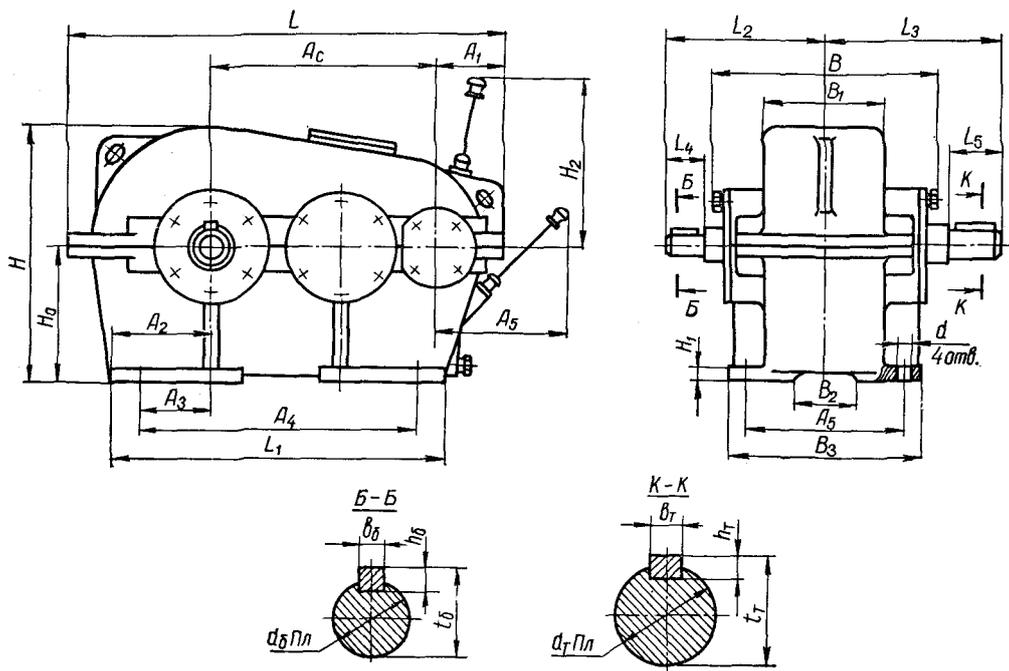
Основные и габаритные размеры редукторов ЦДН.
